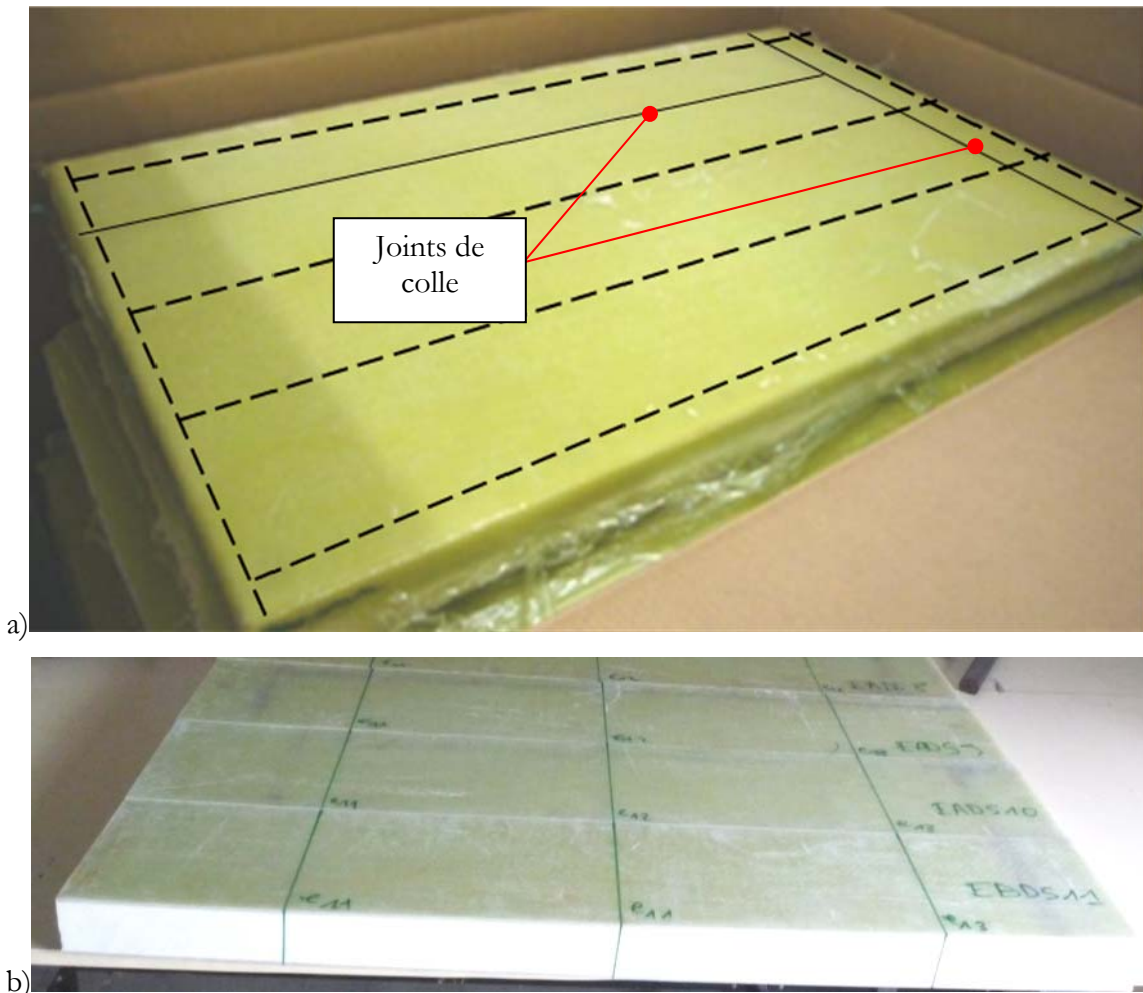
a) ligne de découpe des éprouvettes par jet d'eau ; b) résultat de découpe
